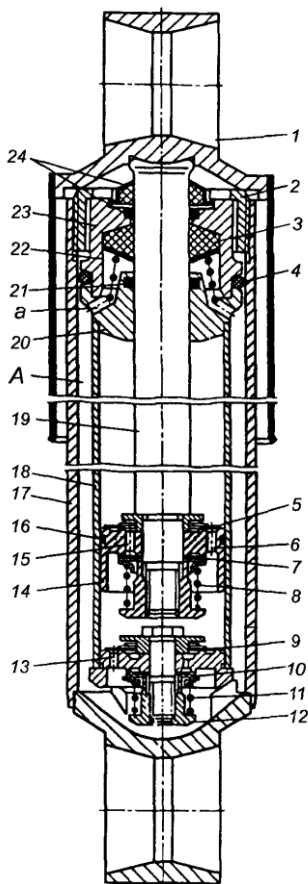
Телескопический амортизатор: 1 – проушина; 2 – гайка резервуара; 3 – уплотнительная манжета штока; 4 – уплотнительная манжета обоймы; 5 – перепускной клапан отдачи; 6 – отверстие наружного ряда; 7 – клапан отдачи; 8, 11 и 22 – пружины; 9 – перепускной клапан сжатия; 10 – клапан сжатия; 12 – гайка; 13 – отверстие перепускного клапана; 14 – поршень; 15 – отверстие внутреннего ряда; 16 – поршневое кольцо; 17 – корпус резервуара; 18 – рабочий цилиндр; 19 – шток поршня; 20 – направляющая штока; 21 – уплотнительная манжета; 23 – обойма уплотнительной манжеты; 24 – войлочные уплотнительные манжеты штока; а – отверстие для слива жидкости в резервуар; А – полость резервуара.
